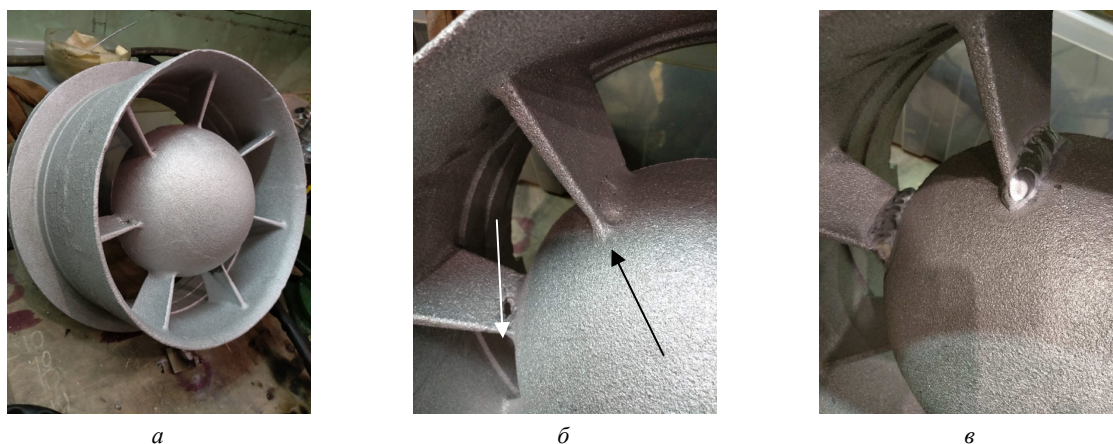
Корпус направляющего аппарата из сплава АК7ч: а – внешний вид изделия; б – дефекты при переходе на различные по толщине части отливки; в – внешний вид исправленных с помощью плазменной сварки дефектов
